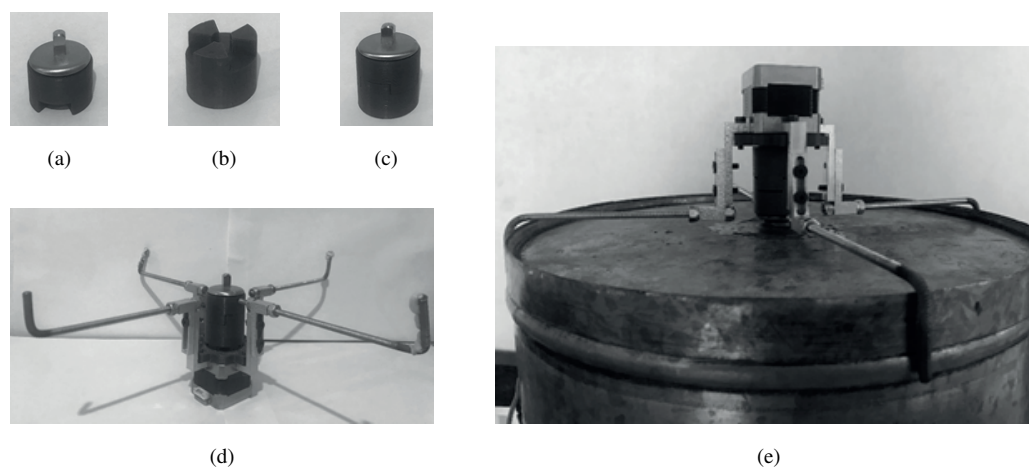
(a) Conector de la propela; (b) Conector del motor; (c) Prensamblado: de los conectores de la propela y el motor; (d) Prensamblado: conjunto de soporte del motor, (e) Acoplamiento conjunto de soporte del motor-propela-recinto
